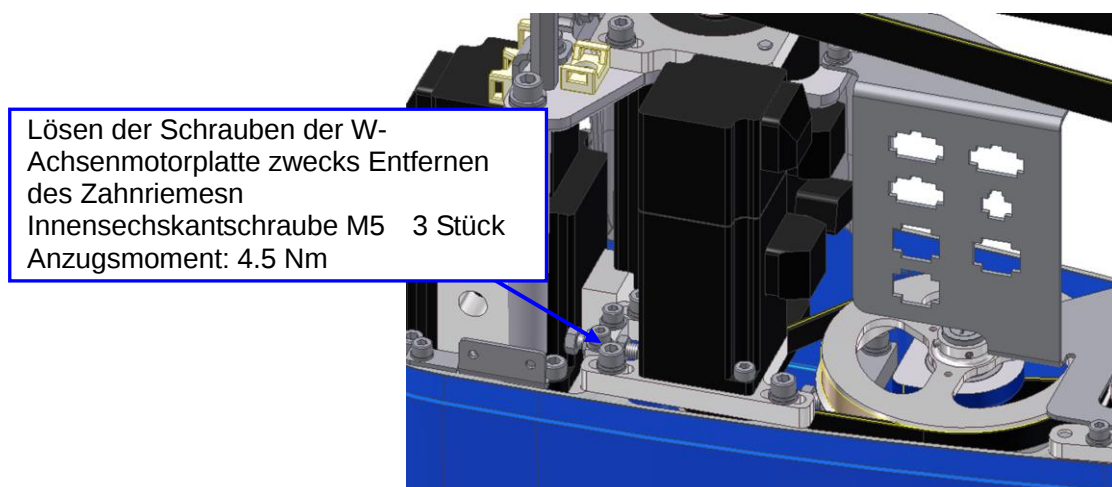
Entfernen des W-Achsen-Zahnriemens
